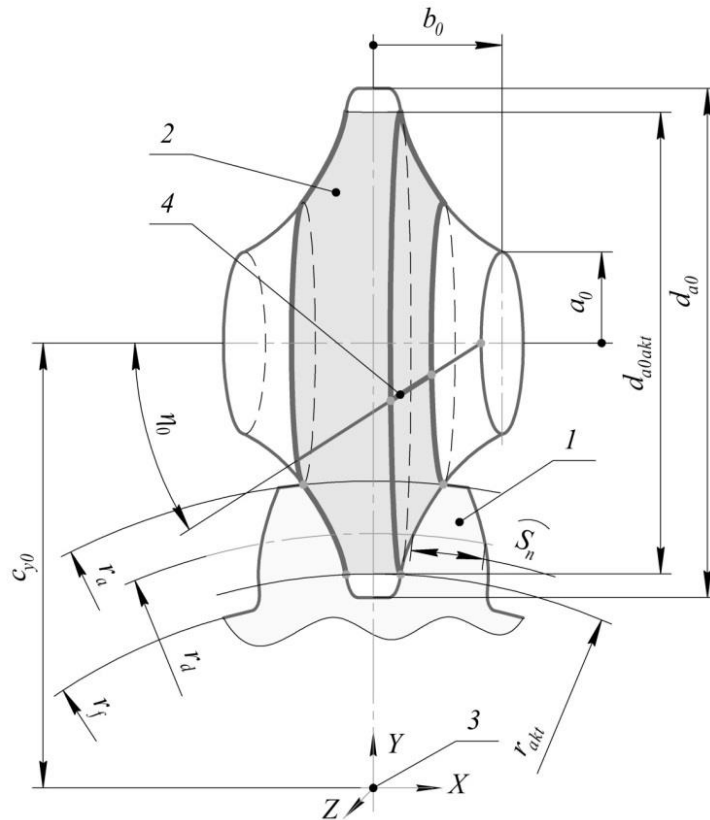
Розрахункова схема визначення параметрів ВІП пальцевої фрези на базі гіперолоїда: 1- зубчасте колесо, 2-поверхня гіперолоїда, 3-вісь зубчастого колеса, 4-прямолінійна твірна гіперолоїда.
